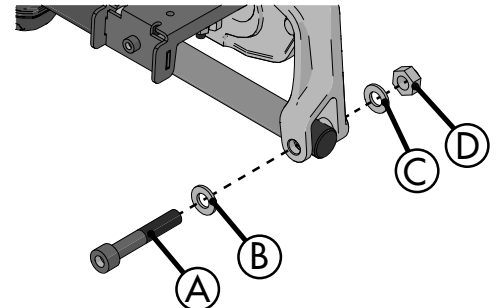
Hintere Befestigung der Stellvorrichtung.
